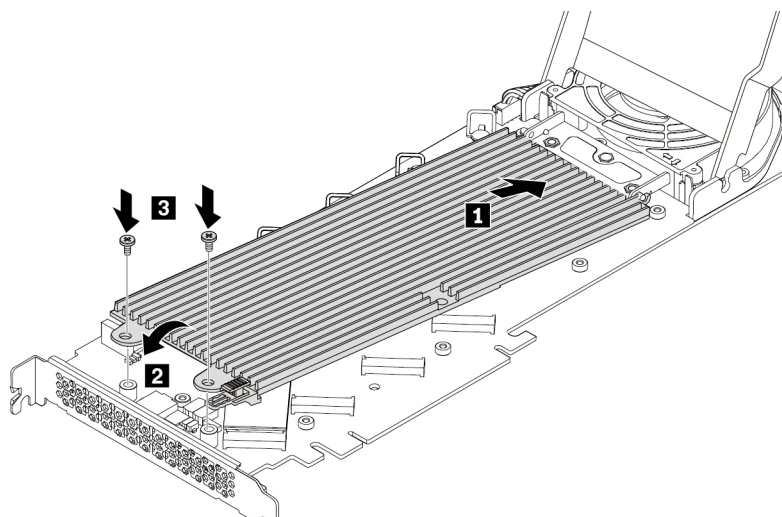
Instalar o dissipador de calor no adaptador PCIe
